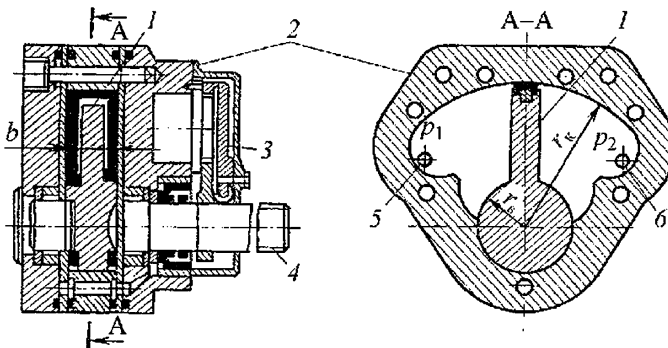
Поворотный гидродвигатель с одной лопастью
